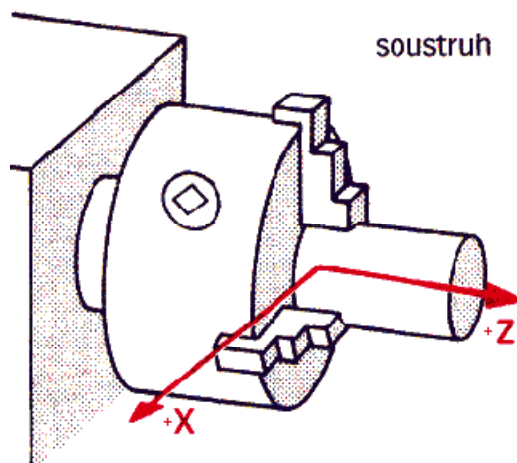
Definování kartézských souřadnic – pravotočivá soustava
